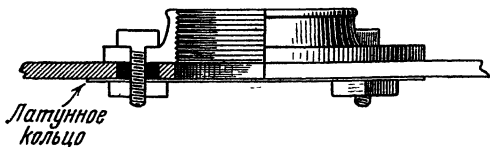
Устройство основания для окулярной трубки, допускающее передвижения с целью регулировки (левая половина показана в разрезе).
